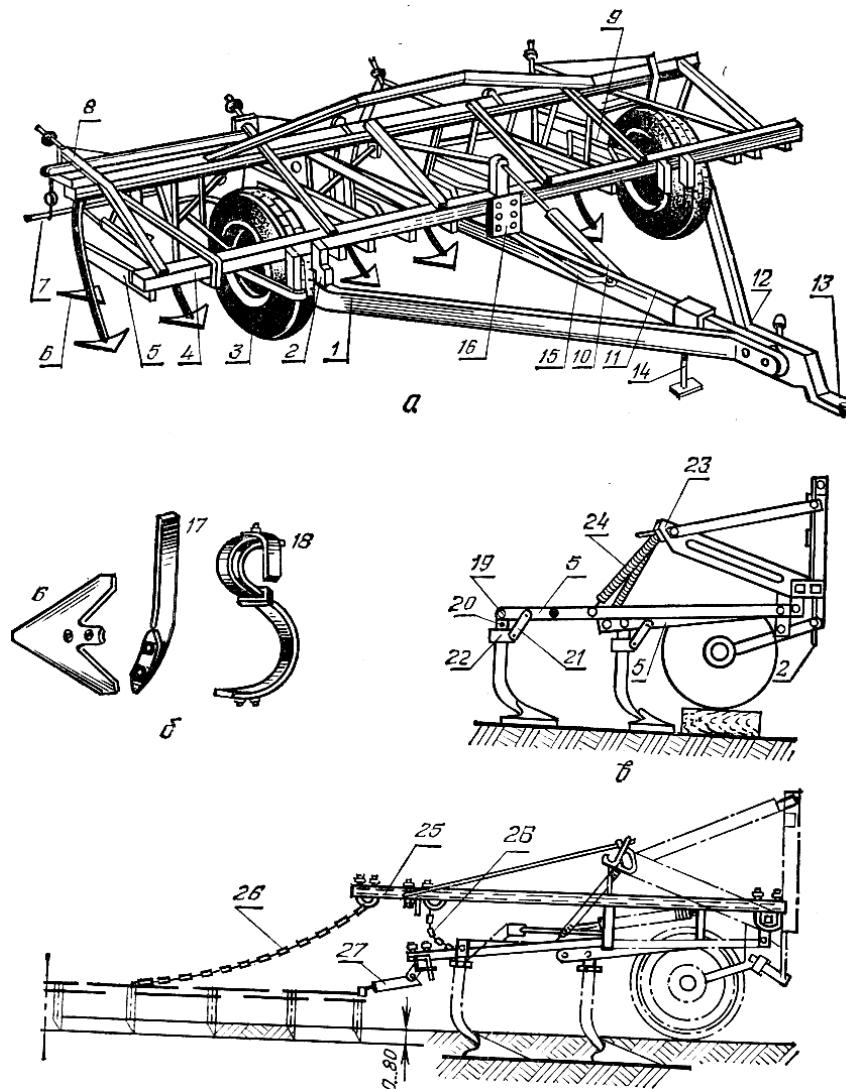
Культиватор КПС-4: а — общий вид; б — рабочие органы; в — секция рабочих органов; г — приспособление для навешивания борон; 1 и 12 — боковые брусья; 2 — регулятор глубины; 3 — ходовое
